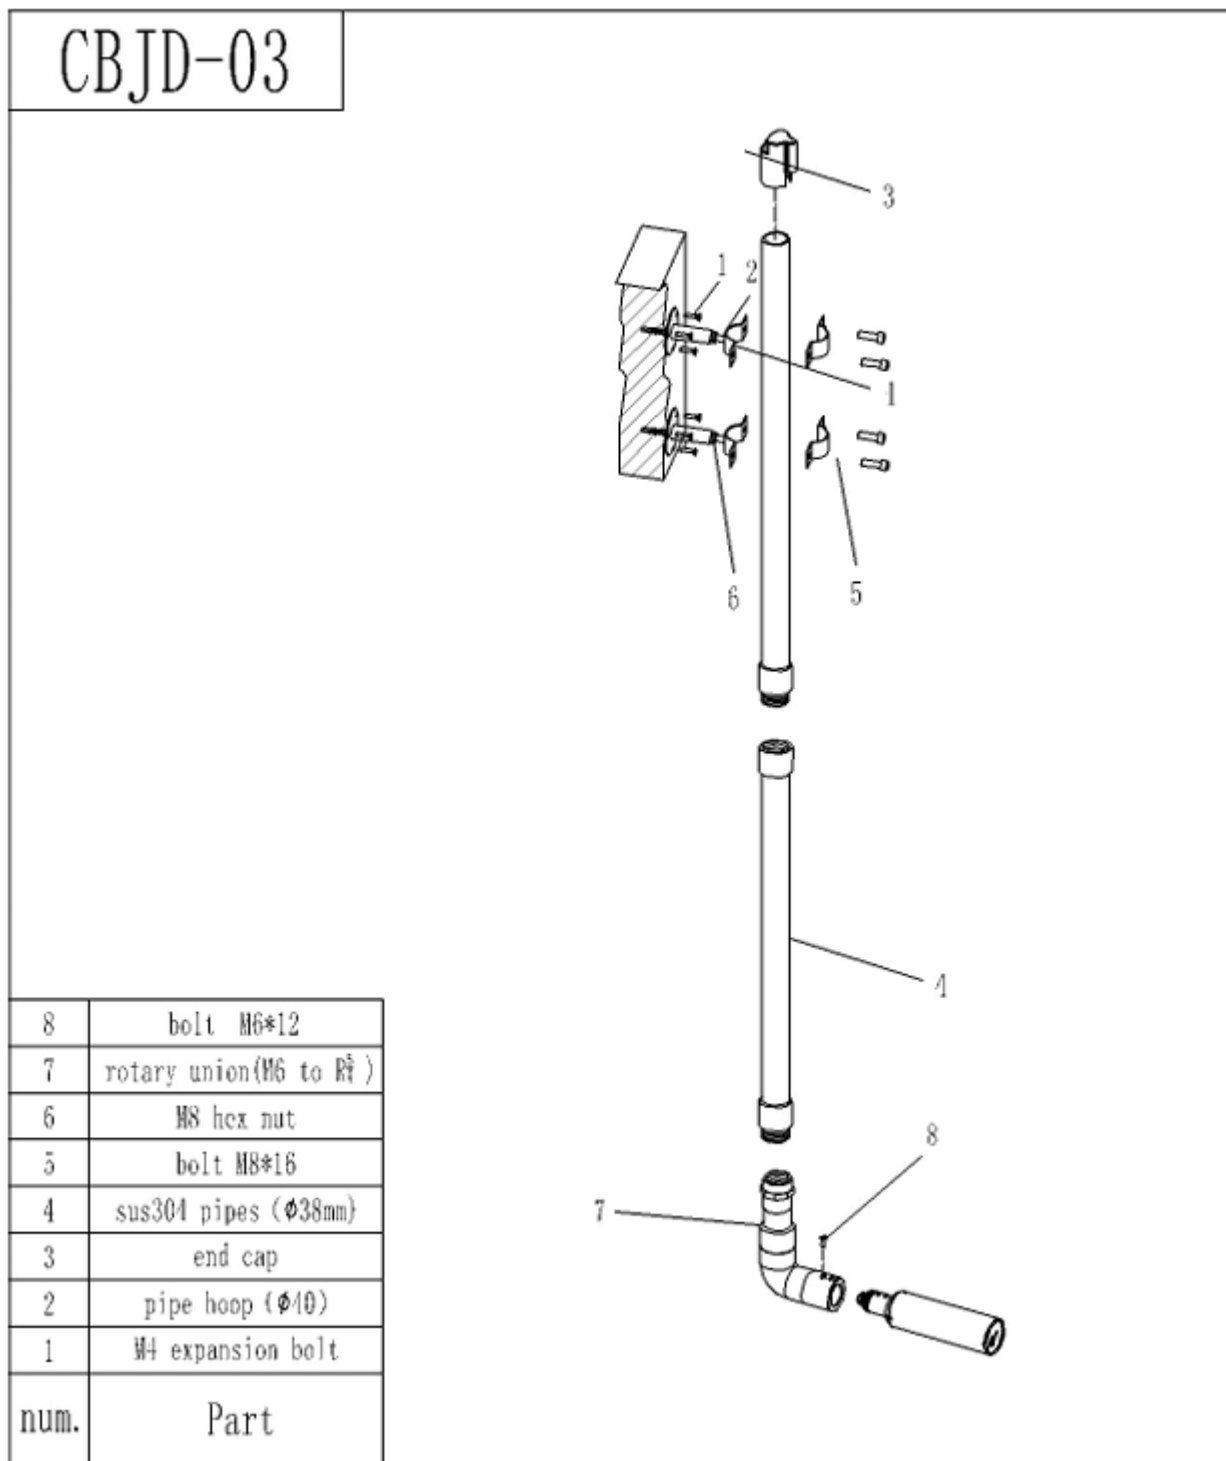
Esquema de instalação fixa clássica à beira do tanque
